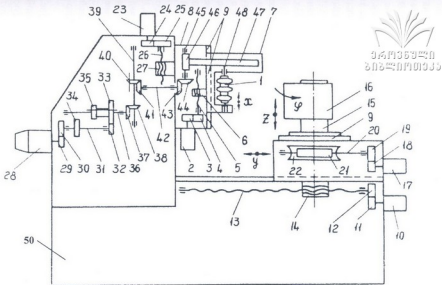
Кинематическая схема зубофрезерного станка с ЧПУ для нарезания некруглых, круглых, спирондных, многовитковых цилиндрических зубчатых колес
